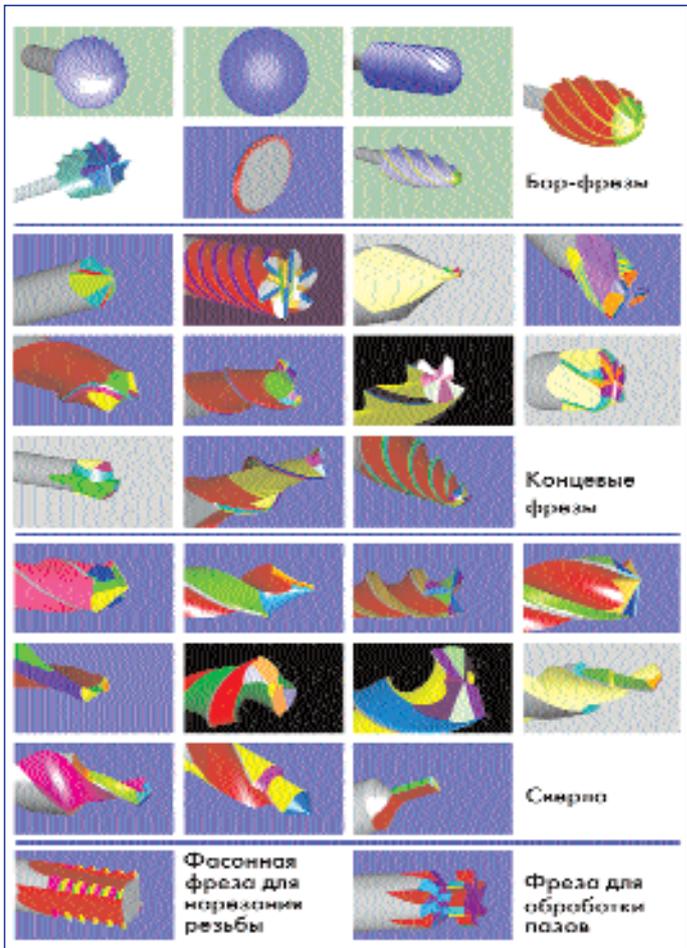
Примеры режущих инструментов, изготовленных на станках Rollomatic
